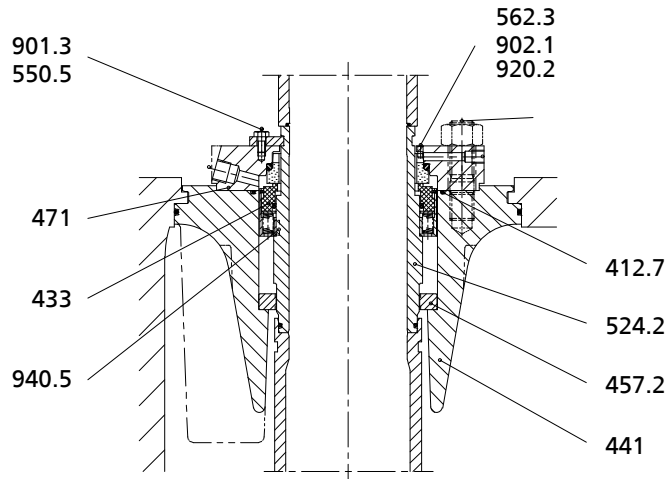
Деталировочный чертеж: Торцевое уплотнение
